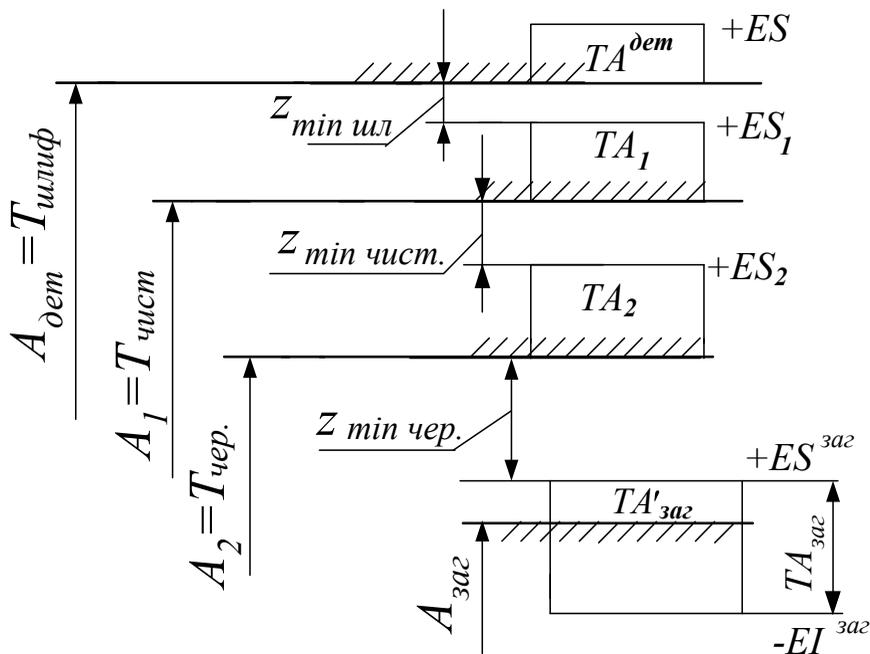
Расчетная схема для определения размера отверстия в заготовке с использованием минимальных припусков (охватывающий размер детали)
